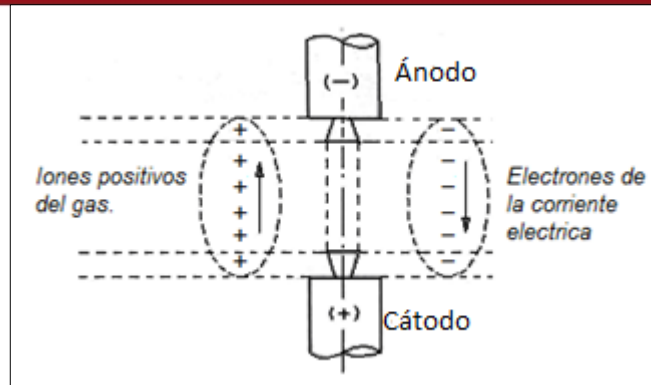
Dirección de viaje de los electrones durante el proceso de soldadura GTAW [4]
